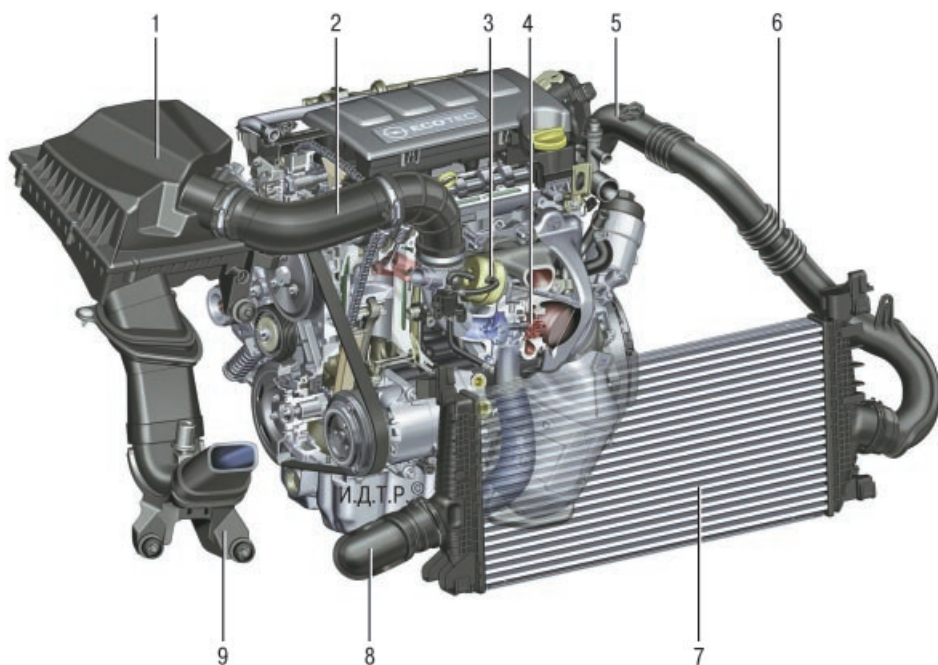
Система подачи воздуха двигателя с турбонаддувом: 1 – воздушный фильтр; 2 – воздухоподводящий рукав низкого давления; 3 – клапан ограничения наддува; 4 – турбокомпрессор; 5 – дроссельный узел; 6 – воздухоподводящий рукав охлажденного наддувочного воздуха; 7 – радиатор охлаждения наддувочного воздуха (интеркулер); 8 – воздухоподводящий рукав горячего наддувочного воздуха; 9 – воздухозаборник
